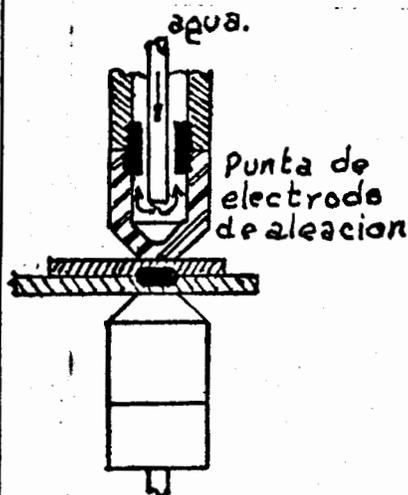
DISPOSICION DE LOS ELECTRODOS Y DE LAS PIEZAS EN LA SOLDADURA POR PUNTOS.
